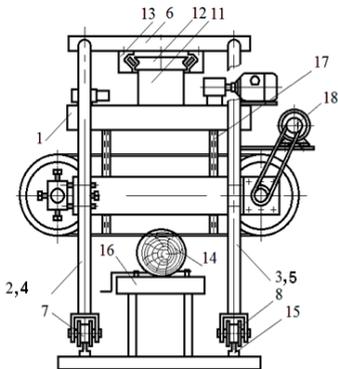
Общий вид ленточнопильного станка (вид спереди)
